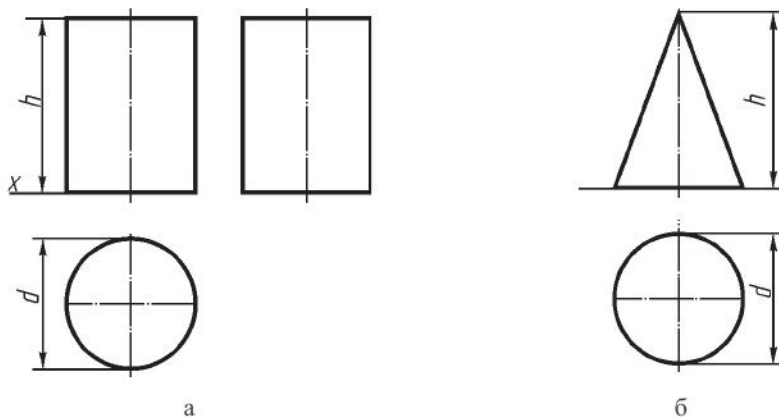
Чертежи: а – цилиндра; б – конуса
